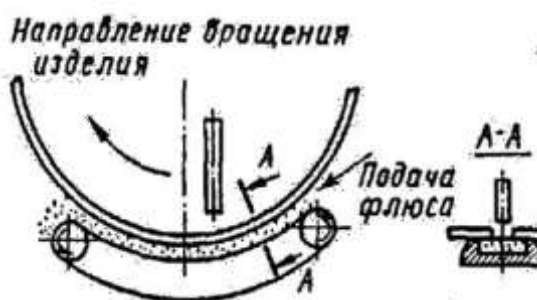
Схема флюсоремненной подушки для сварки кольцевых стыков
